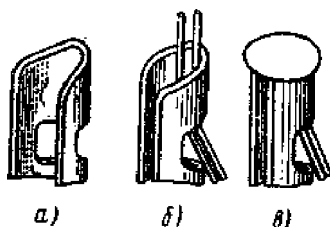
Последовательность выполнения сварного соединения
